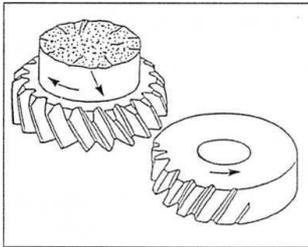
wälzstoßen einer Schrägverzahnung vom Schrägungswinkel der Verzahnung,
